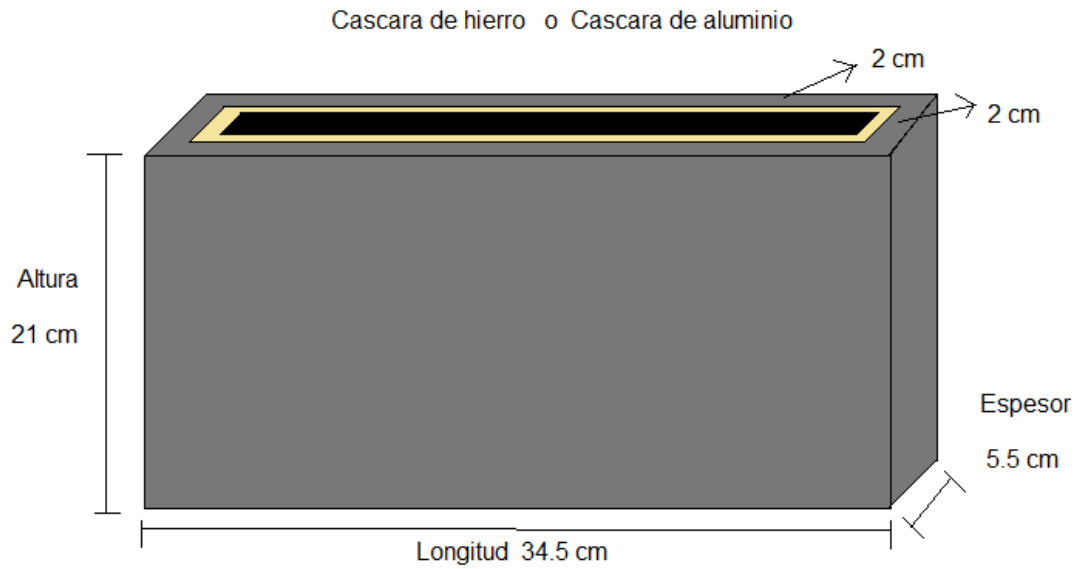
Dimensiones de la Cascara de hierro y de aluminio.
